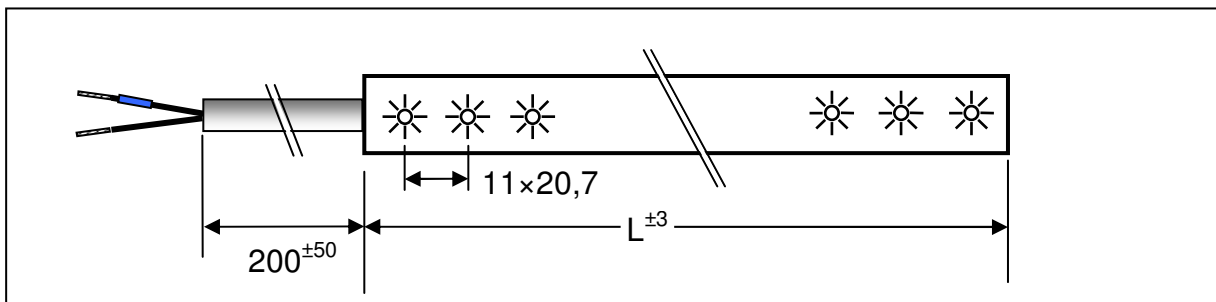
Einseitiger Anschluss (Gehäusevarianten)
